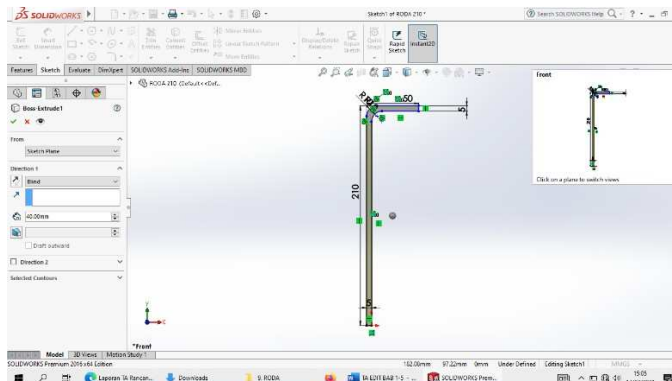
22 Hasil 3D Modeling Plat Roda Penggembur
